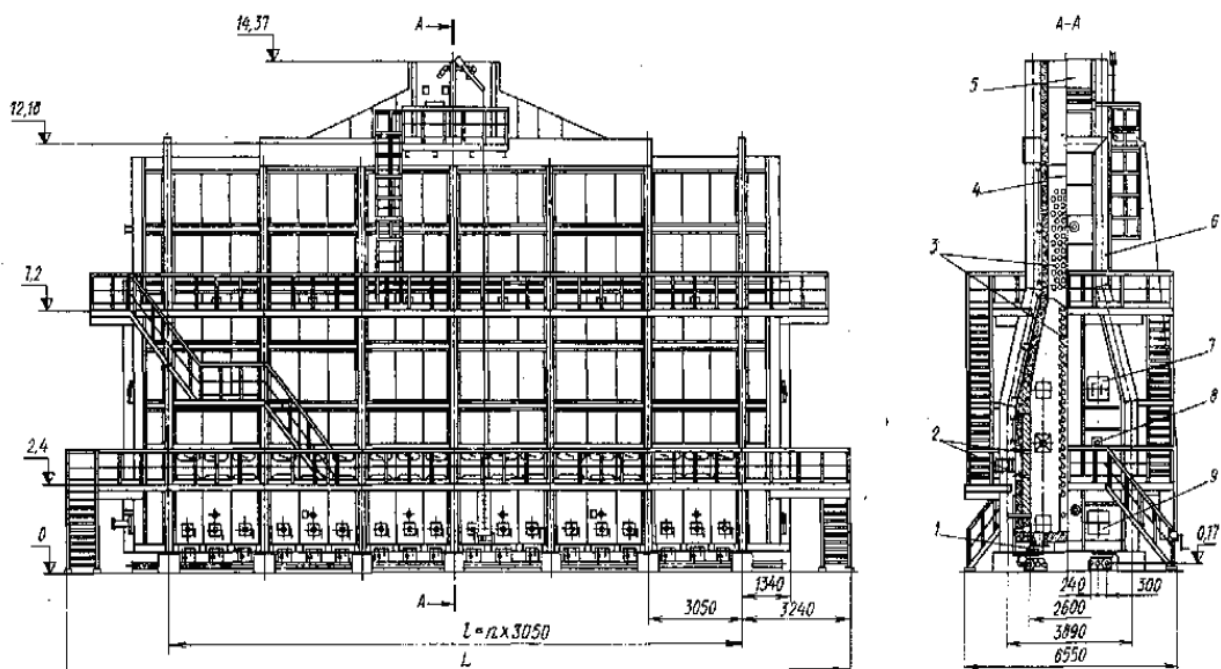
Конструкция трубчатой печи типа ЗД: 1 – горелка; 2 – каналы для подвода воздуха; 3 – змеевики; 4 – футеровка; 5 – газосборник; 6 – каркас; 7, 8 – выхлопное и смотровое окна; 9 – люк-лаз
